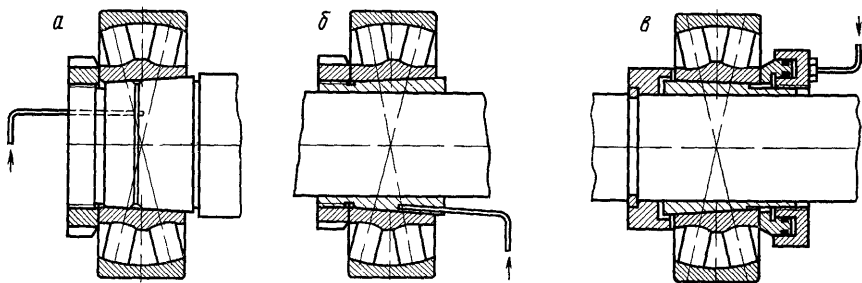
Типовые примеры гидропрессового способа монтажа подшипников
